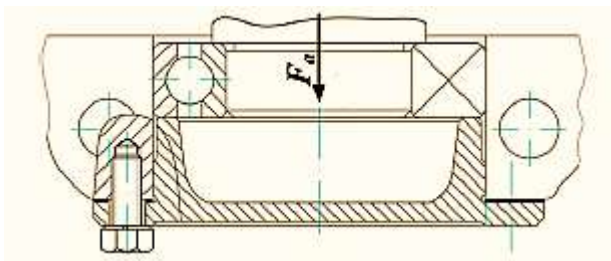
Эскиз к расчету винтового соединения крышки с корпусом редуктора
